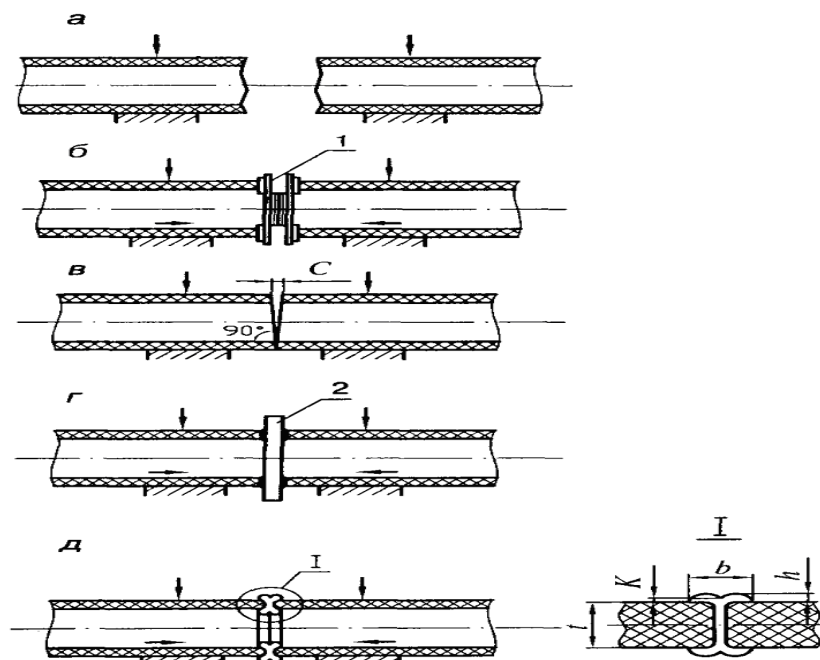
Последовательность выполнения операций при сварке труб нагретым инструментом: а – центровка и закрепление в зажимах сварочной машины концов свариваемых труб; б – механическая обработка торцов труб с помощью торцовки 1; в – проверка соосности и точности совпадения торцов по величине зазора С; г – плавление и нагрев свариваемых поверхностей нагретым инструментом 2; д – осадка стыка до образования сварного соединения
